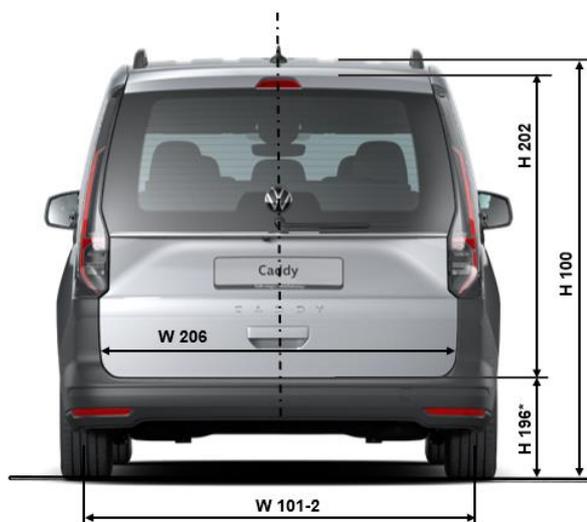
Dimensioni Caddy o Caddy Maxi, vista posteriore (conforme a DIN70020, T1)
